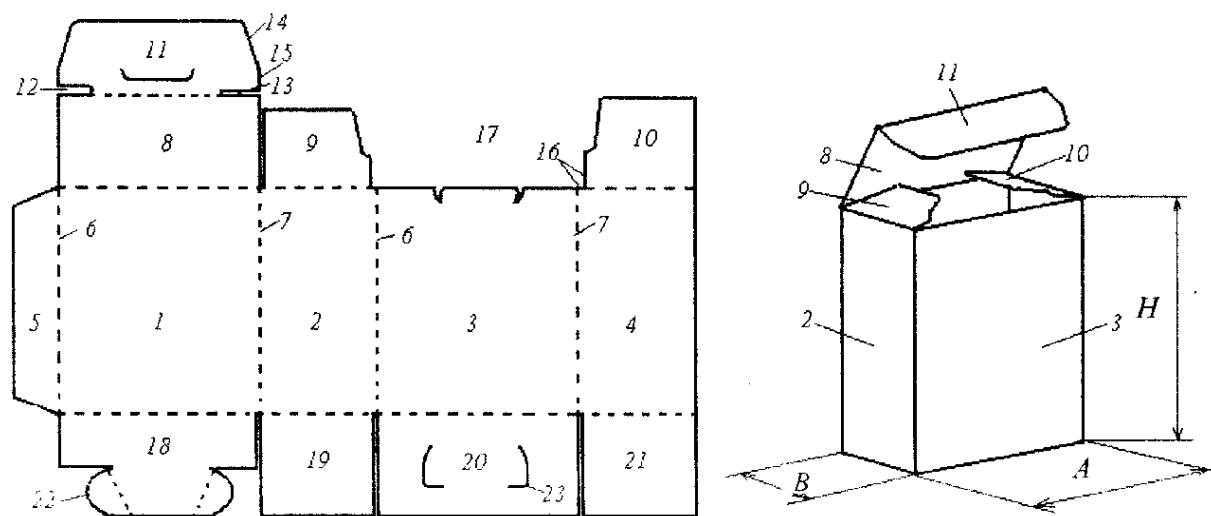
Основные и вспомогательные элементы развертки коробки и ее вид после сборки:
